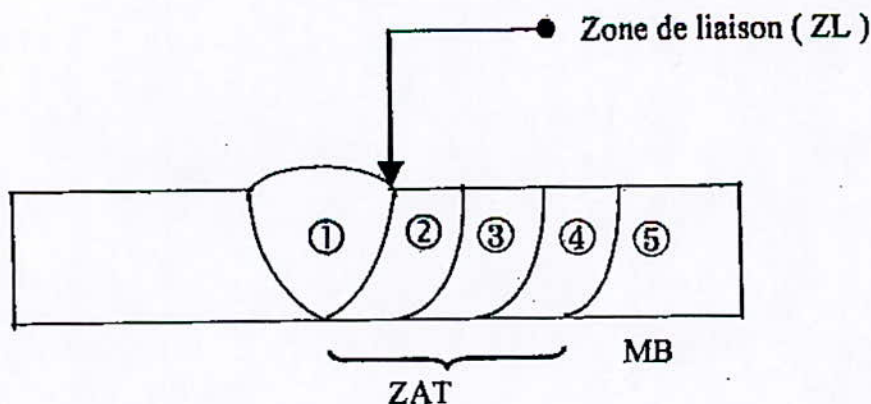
Les différentes zones d'un assemblage soudé.
